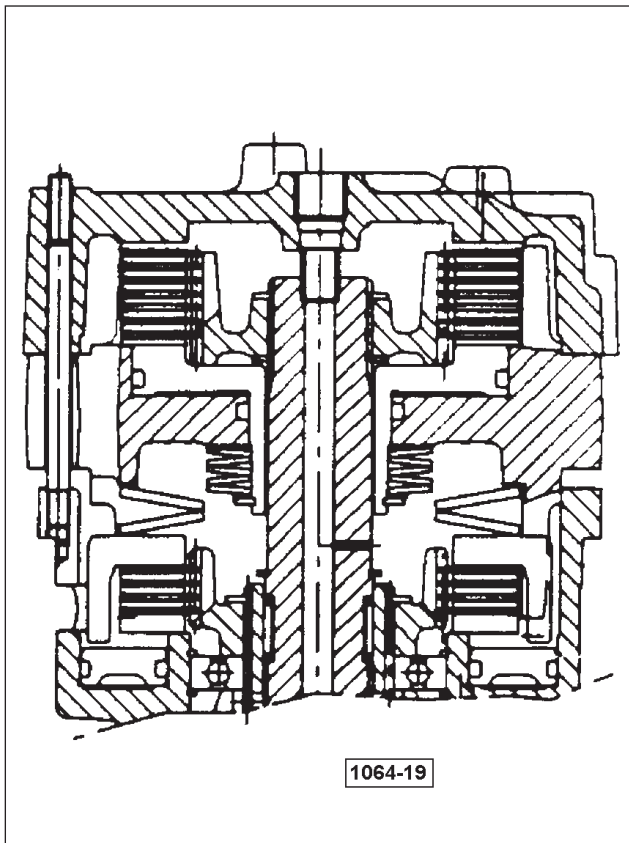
Prémontage des pièces sur l'arbre "MEDIUM".
